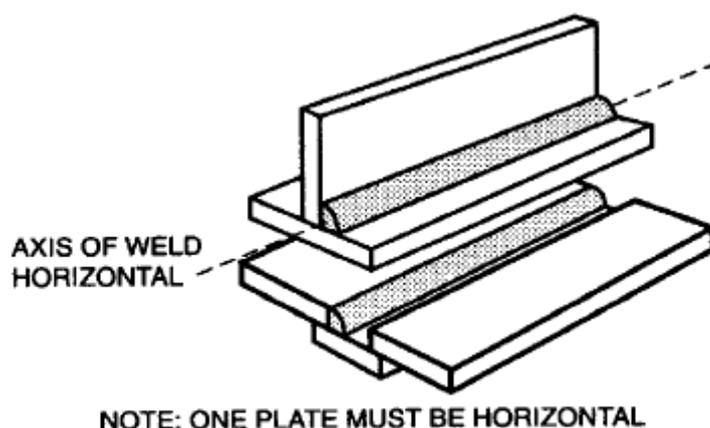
Posición horizontal (2F) para soldaduras de filete.
